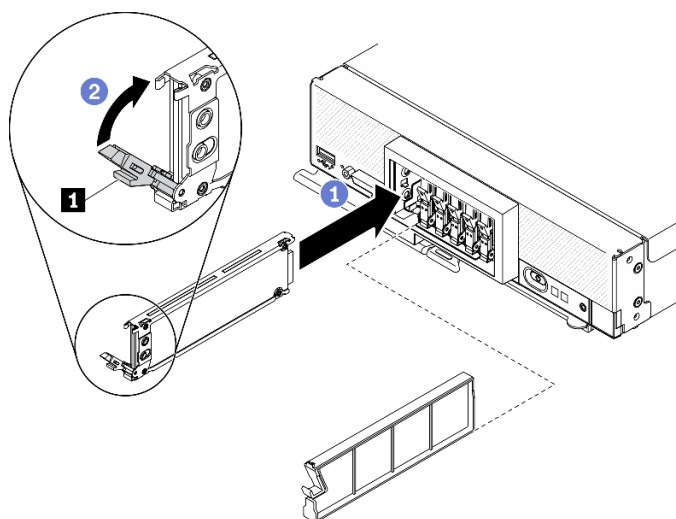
Installation d'une unité remplaçable à chaud EDSFF
